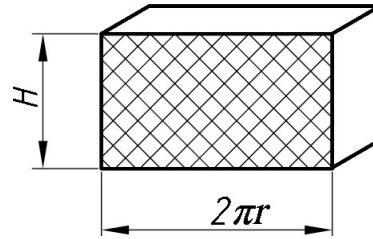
Схема развертки образовавшегося цилиндра:
